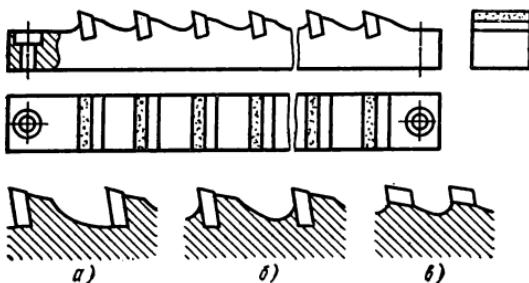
Крепление твердосплавных пластин к корпусу протяжки методом пайки
